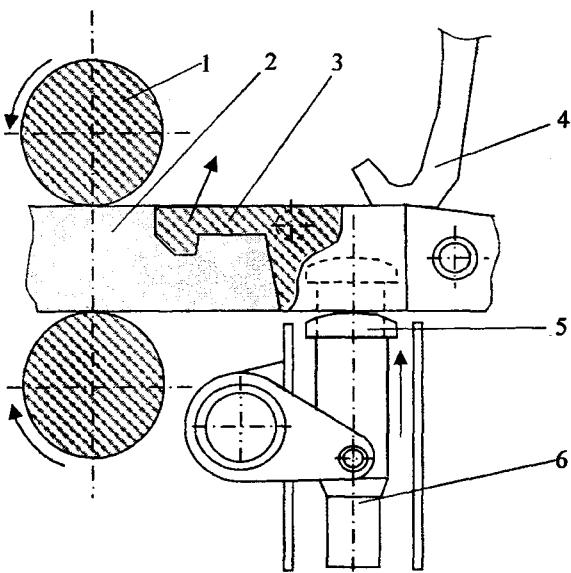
Схема устройства для отделения головки затравки от сляба: 1 – ролик; 2 – сляб; 3 – головка затравки; 4 – крюк захвата; 5 – упор; 6 - гидроцилиндр
